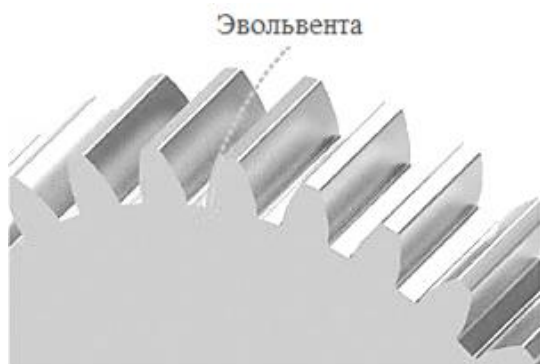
Зубчатое колесо с эвольвентным профилем
